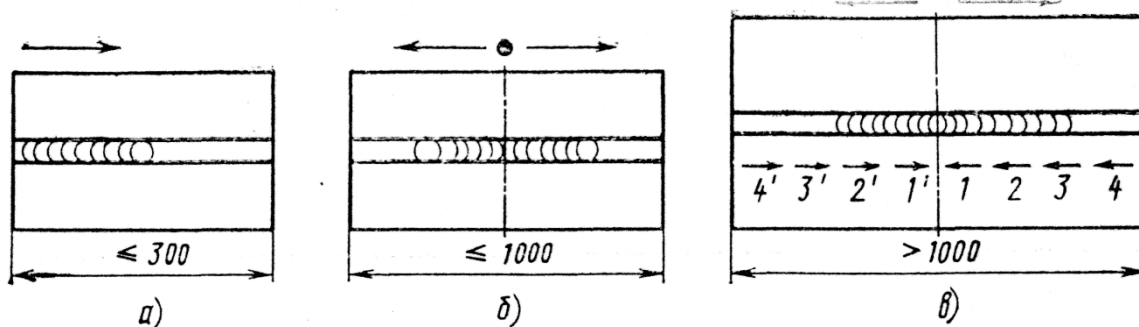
Послідовність зварювання швів різної довжини (стрілками вказано напрямки зварювання):
